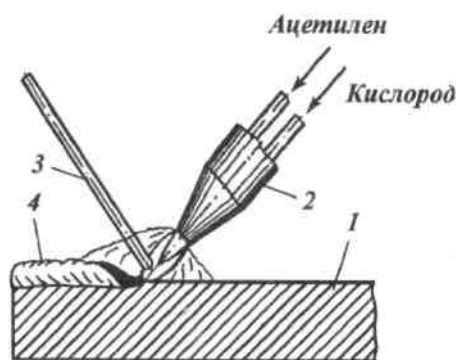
Схема газовой наплавки: 1 - наплаваемая деталь; 2 - газовая горелка; 3 - присадочный материал; 4 - наплаваемый металл
